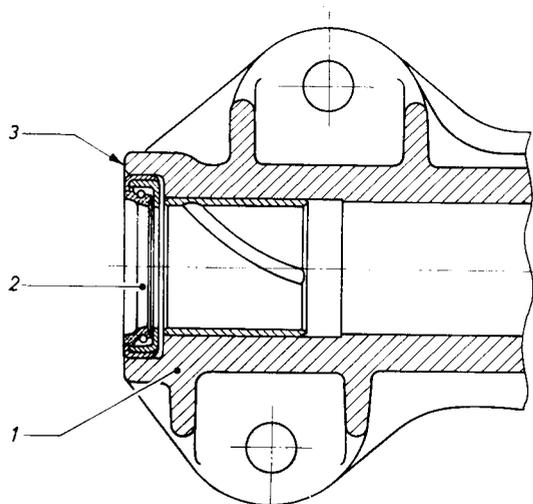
Öldichtring für Lenkstockwelle im Lenkgehäusehals
